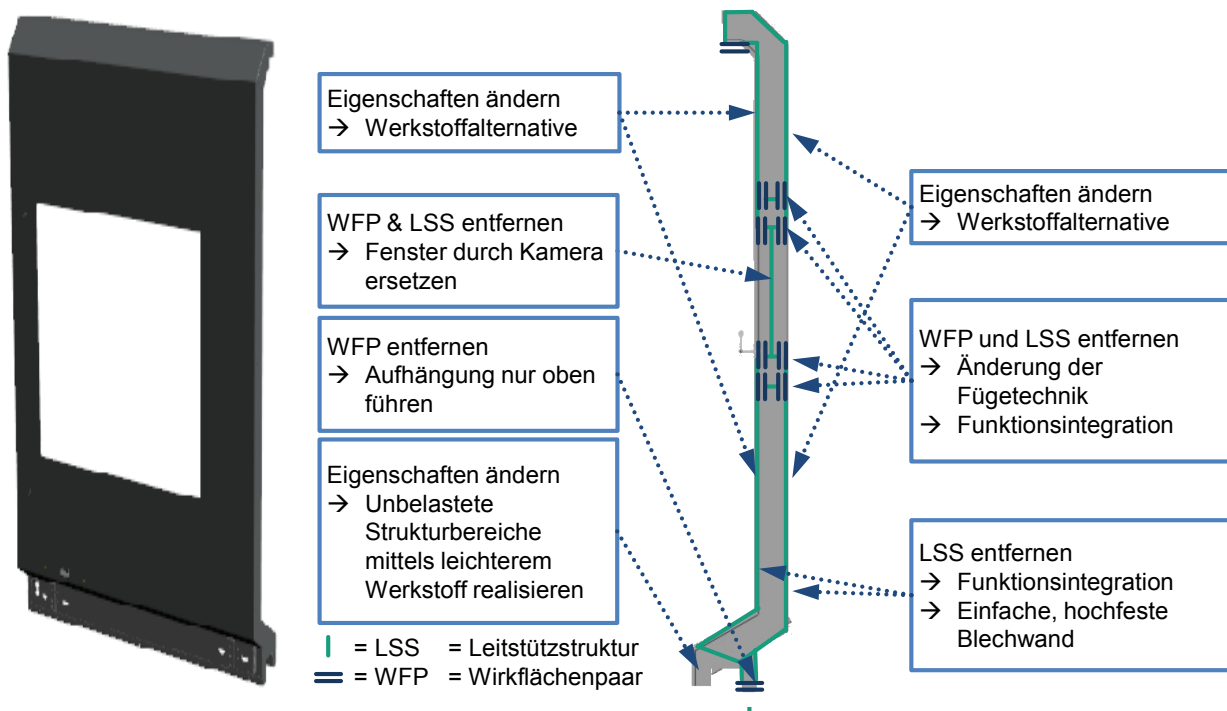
Anwendung der Leichtbau-Denkwerkzeuge auf eine Maschinenschutztür
